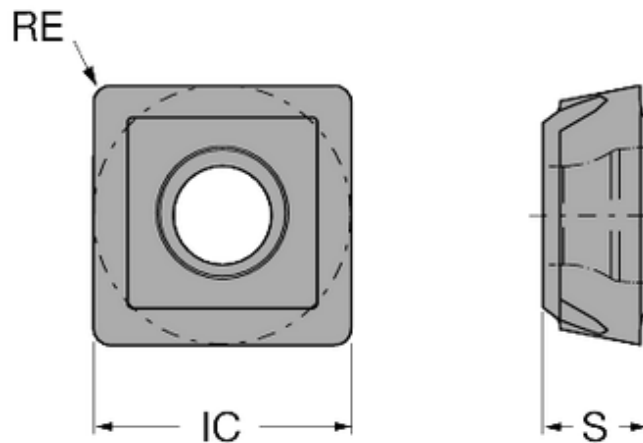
Пластинка ріжуча 880-06 04 W10H-P-GR 4334
